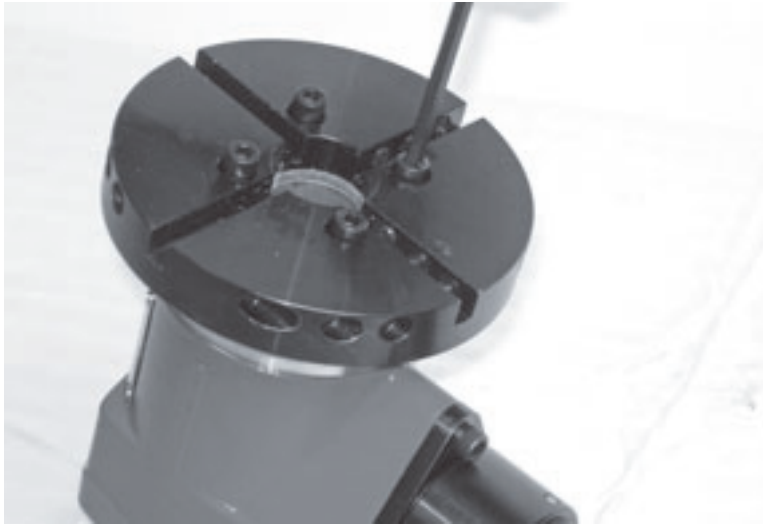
Entfernen Sie die Schrauben des rotierenden Werkzeugkopfs mit einem 3/16-Zoll-Sechskantschlüssel.
